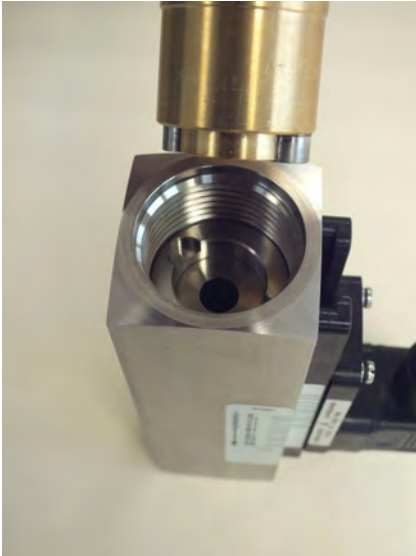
Eindrehwerkzeug Gewindering (Eingang) einführen
